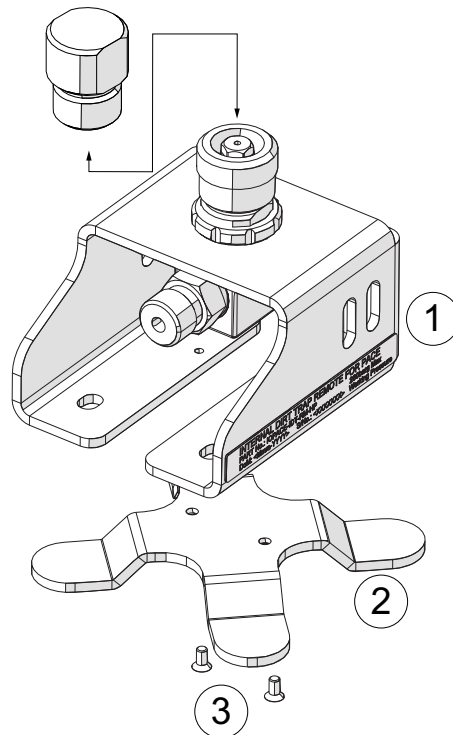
Anbringen oder Entfernen des Standes vom Halterung
